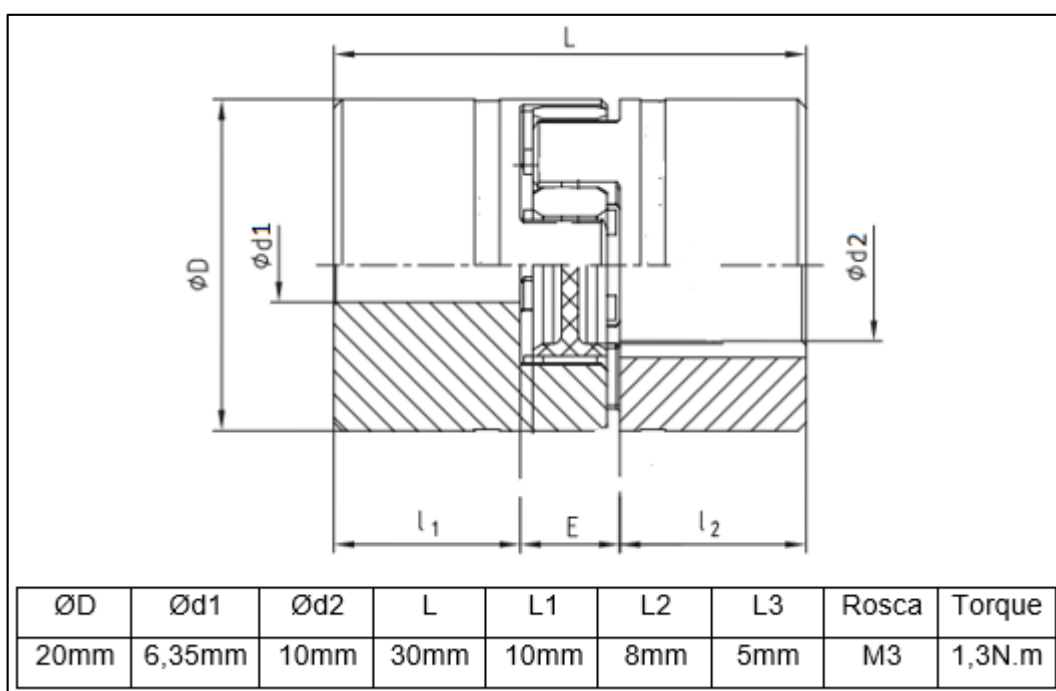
Desenho e dimensões do acoplamento flexível
